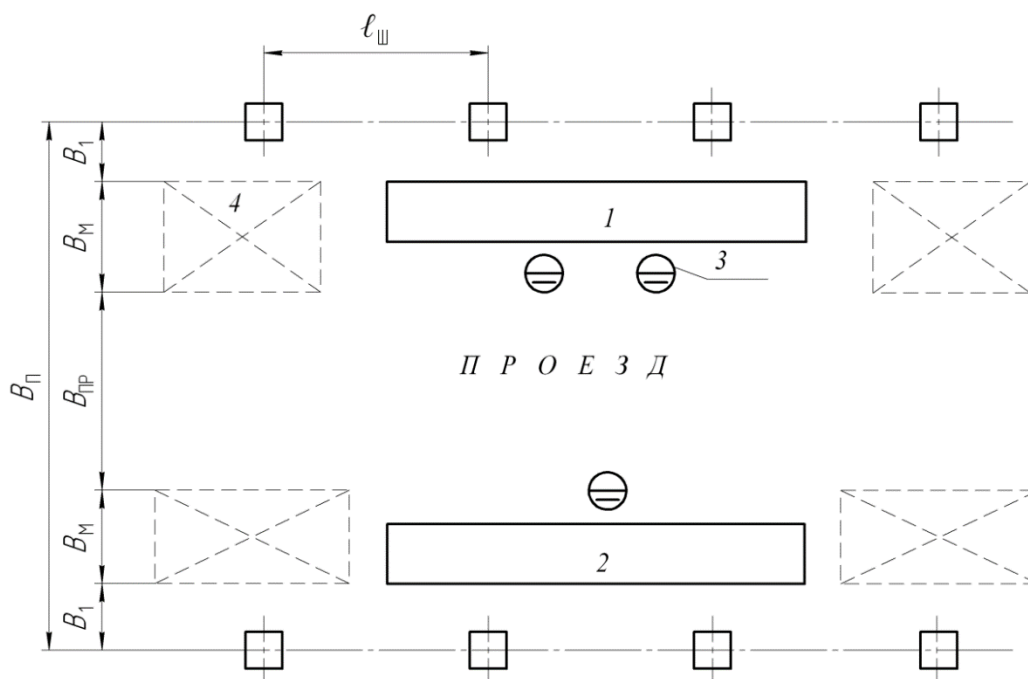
Схема планировки цеха при расположении складочных мест между рабочими местами: 1 – участок резки металла; 2 – сборочно-сварочный стенд; 3 – место обслуживающего персонала; 4 – складочное место
